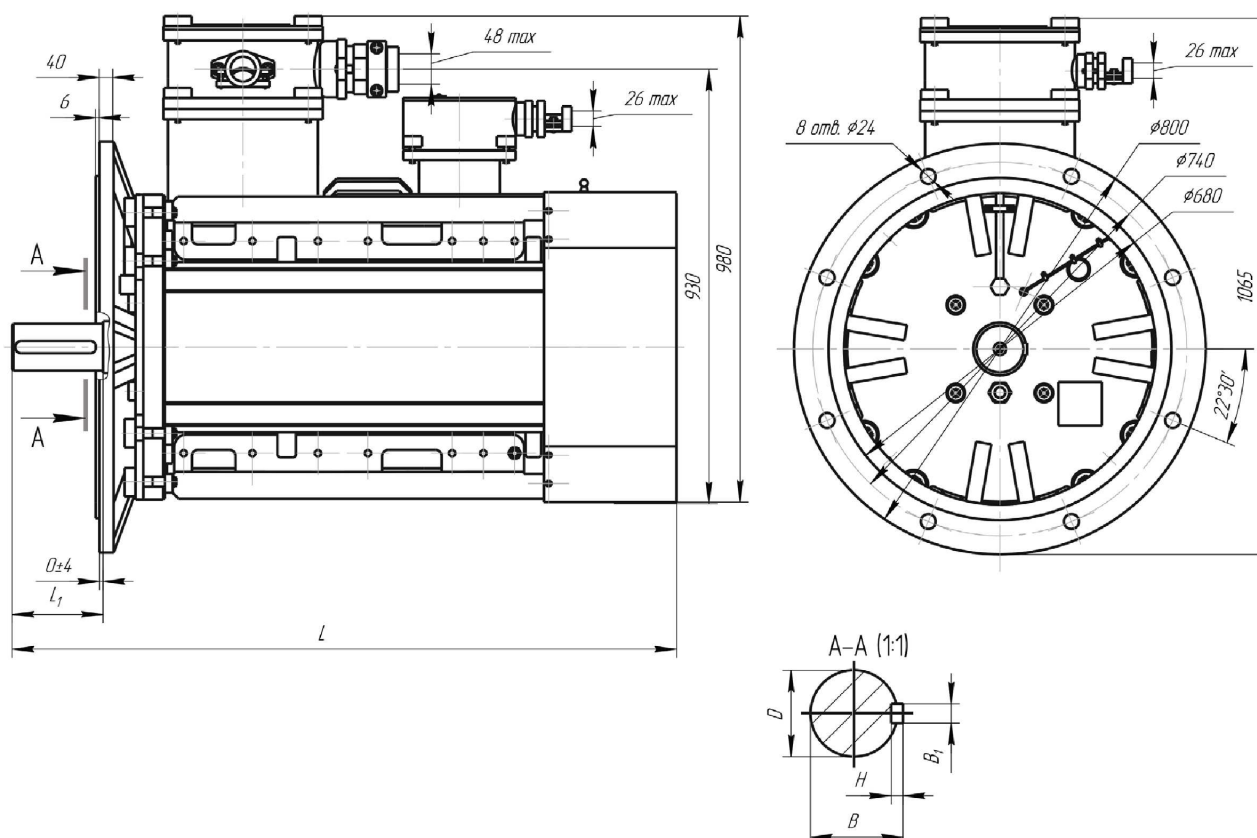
Габаритные и установочно-присоединительные размеры электродвигателей ВАО7А(М)-315(355) IM3001 (с фланцем на щите, доступным с обратной стороны)
